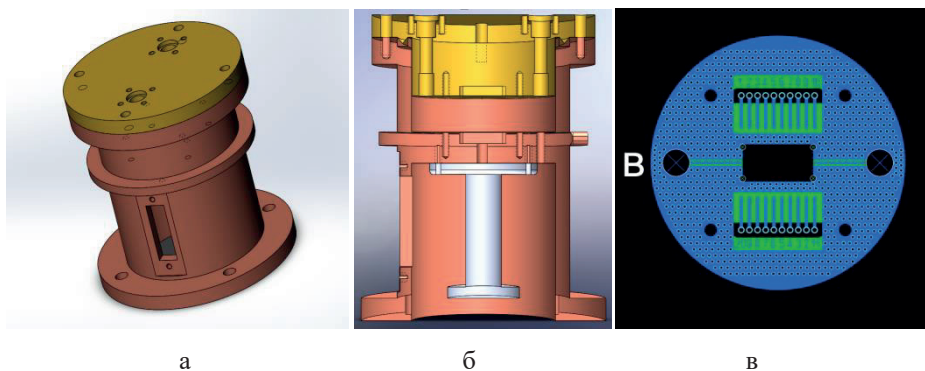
Модель держателя образцов: а – общий вид, б – в разрезе. Плата для образца – в
